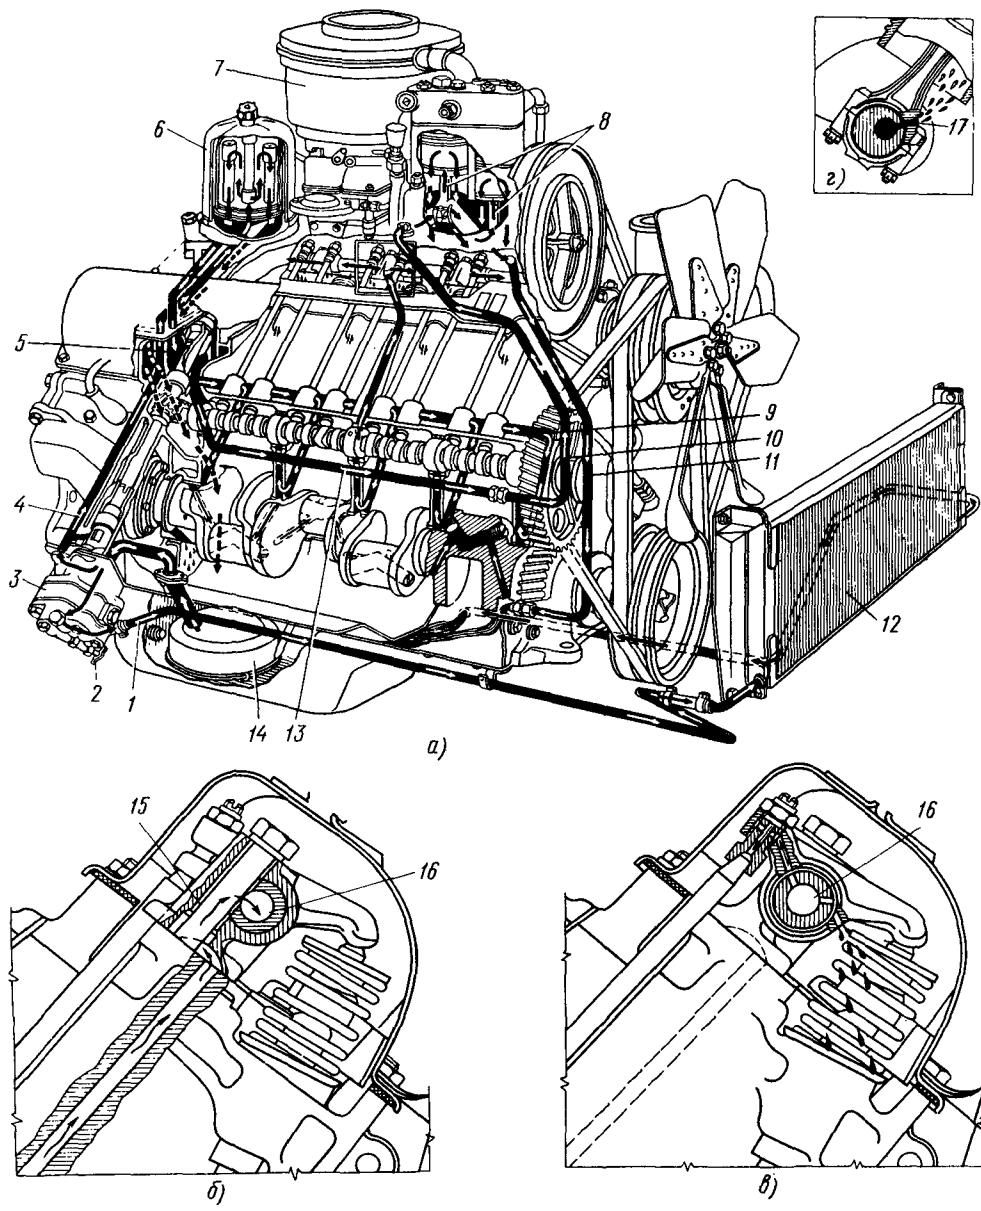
Схема системы смазки двигателя ЗИЛ-130:
